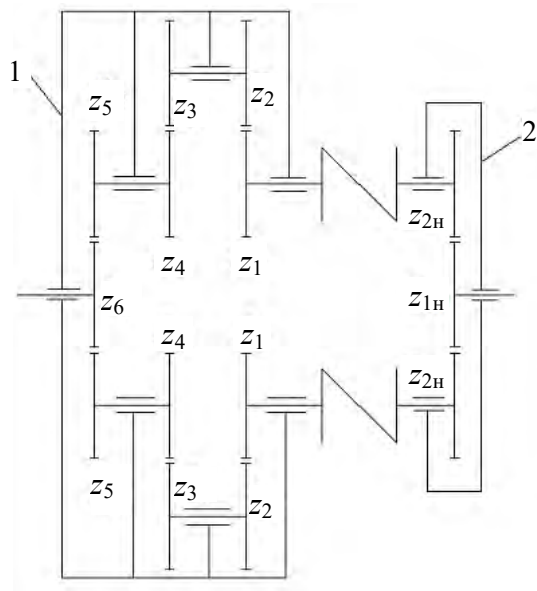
Кинематический контур из валов и зубчатых передач обкатываемого редуктора 1 и механизма нагружения 2
